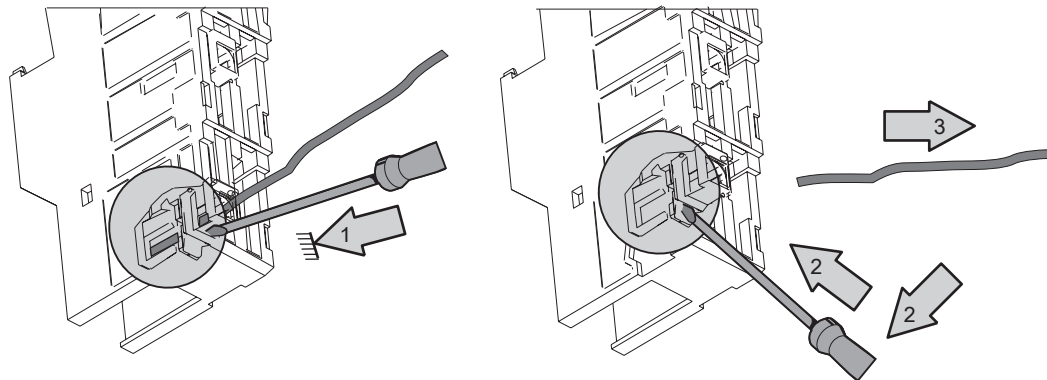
Verdrahtung beim Terminalmodul mit Fast Connect lösen
